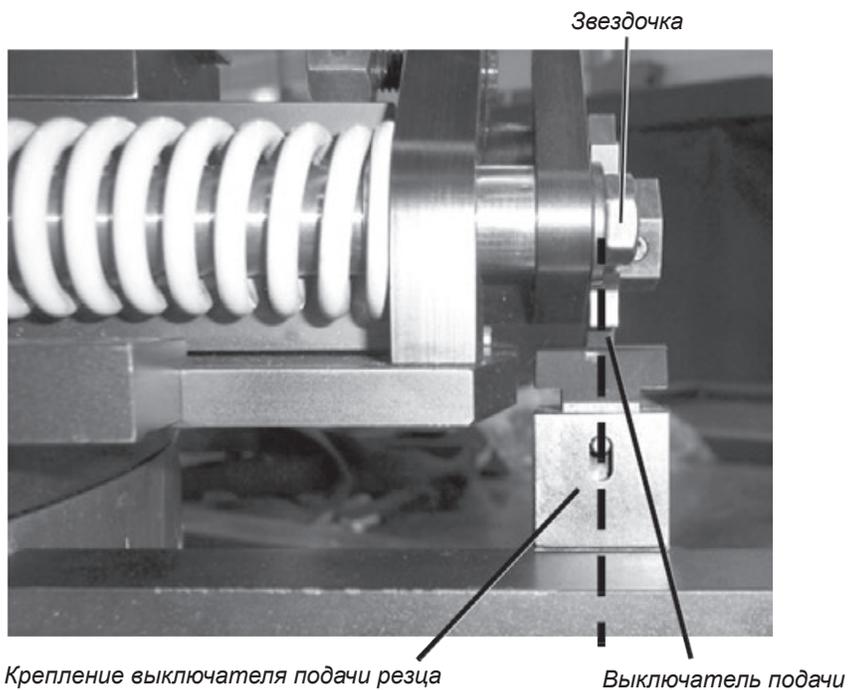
Расположите крепление выключателя подачи, обеспечив нахождение контактных точек звездочки по центру выключателя.
